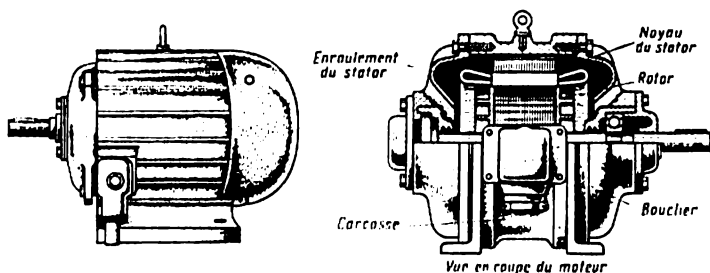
Vue d'ensemble et en coupe d'un moteur asynchrone à rotor en court-circuit
